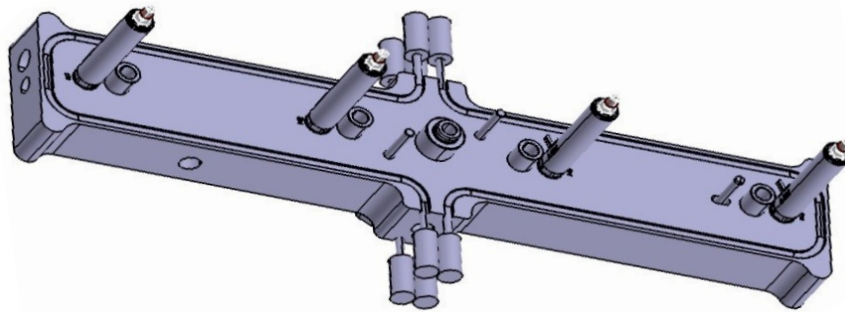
Horký systém s uzavíratelnou jehlou [27]
